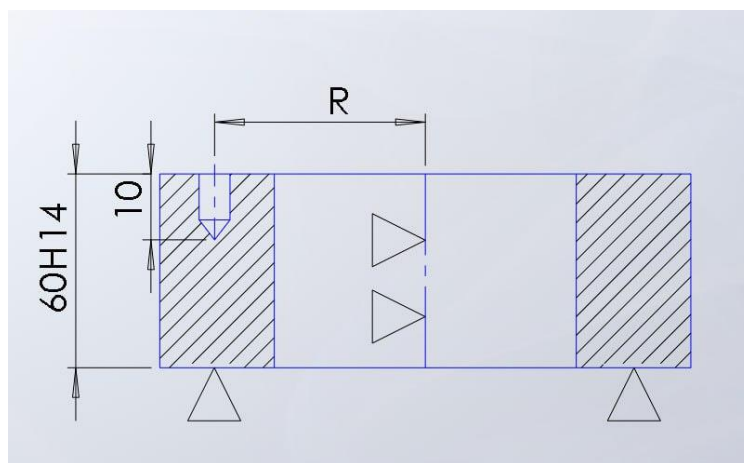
Визначення похибок базування для верстатного пристрою
